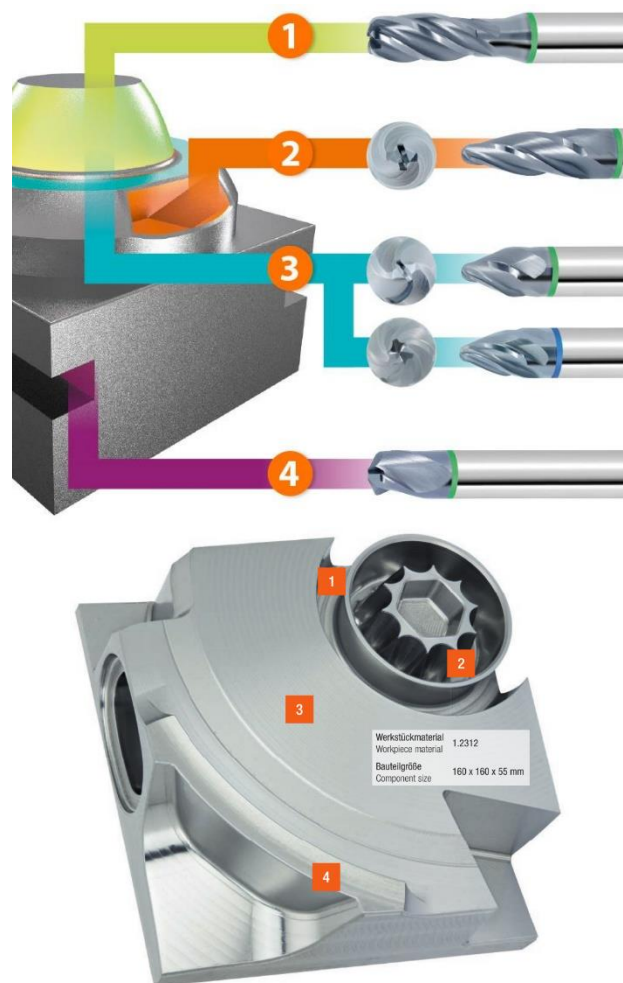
Porovnání geometrie kulové a soudečkové frézy [30]
